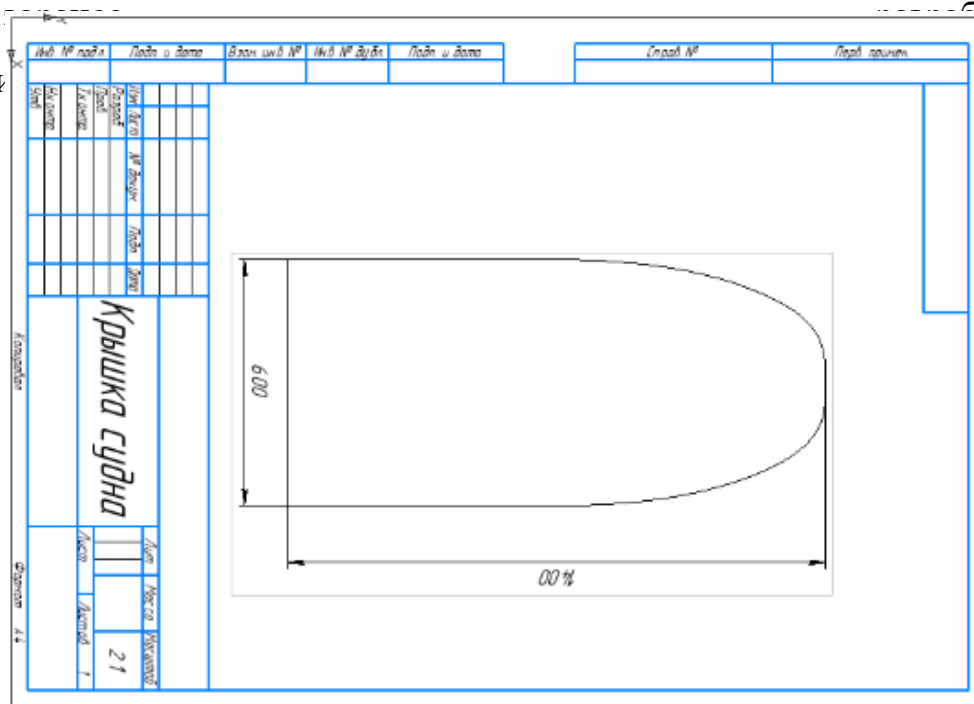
Подготовка чертежей для лазерного станка (резка)
